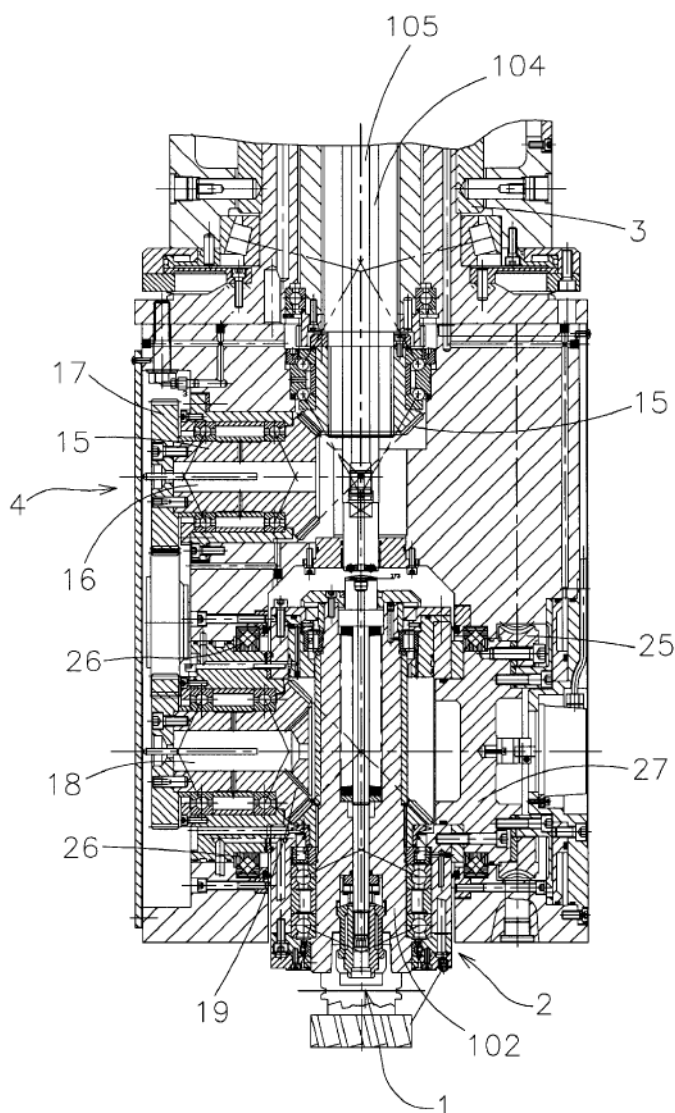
Řez vidlicovou hlavou s elektrovřetenem, torque motorem a planetovou převodovkou [16]
